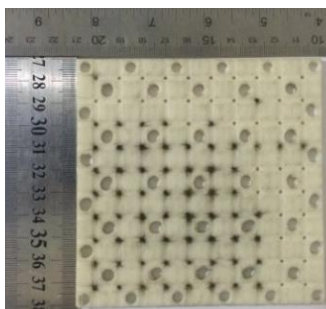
Suporte de soldagem impresso em ABS, com região interna no formato da malha projetada.
